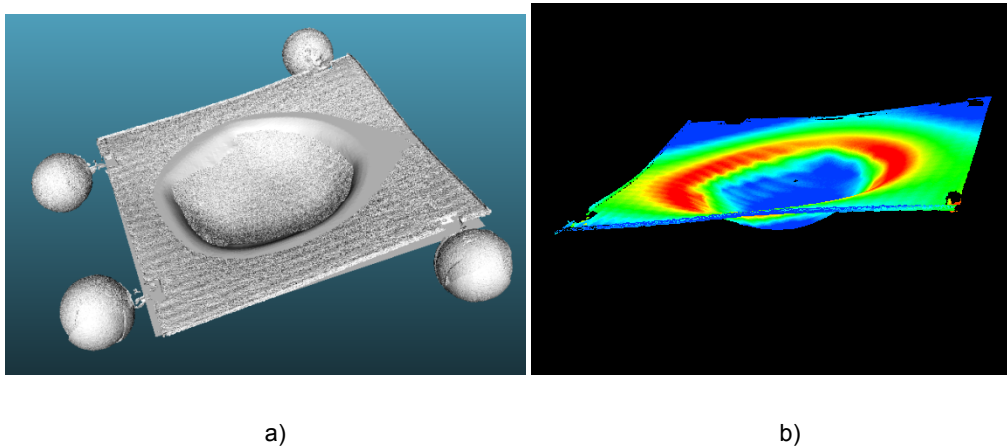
a) superposició de pròtesi experimental amb la teòrica b) exemple de la variació dimensional
